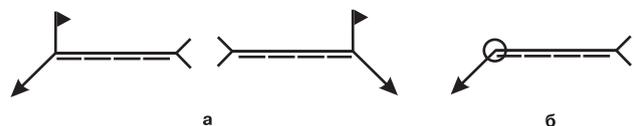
Условные обозначения типа сварного шва
